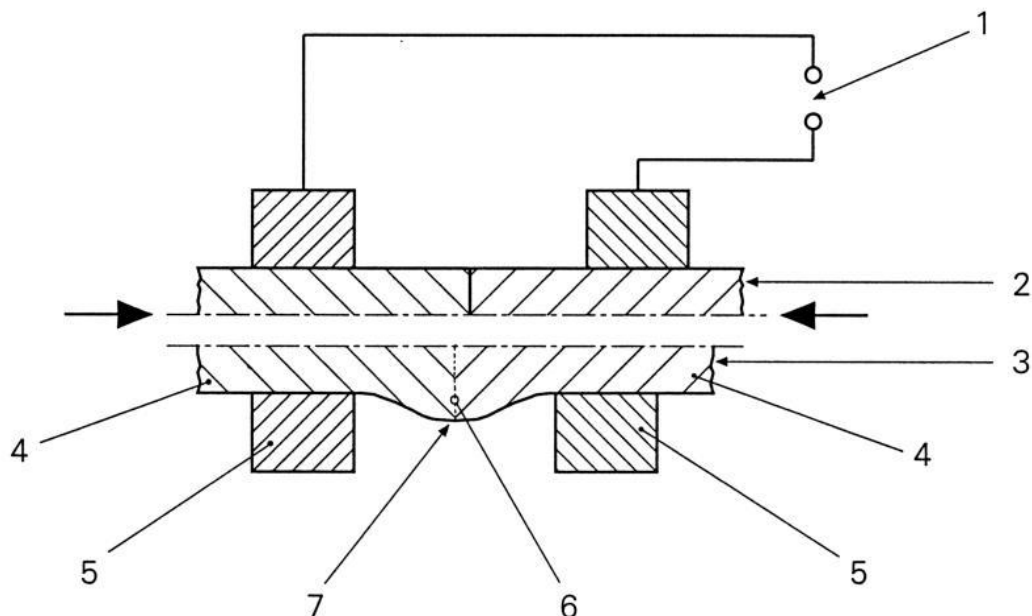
Princípio de trabalho para solda a topo de resistência a pressão
